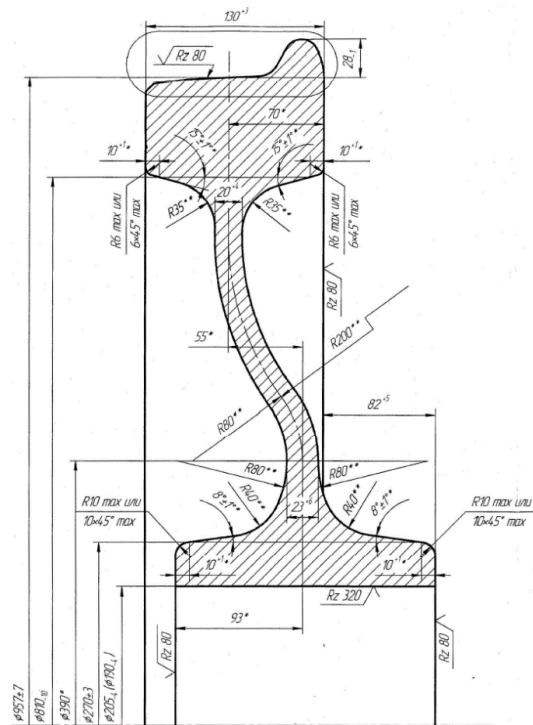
Колеса железнодорожного подвижного состава, изготовленные по чертежам:
